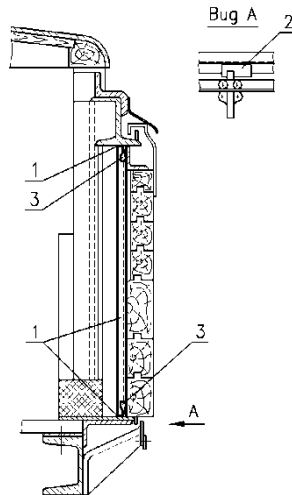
Заделка зазоров двери вагона, используемой для погрузки, бумагой
